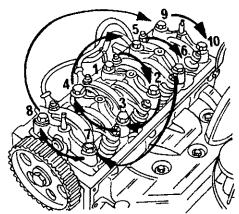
Схема затяжки болтов головки цилиндров на двигателе типа TU (с или без рабочих гильз цилиндров).
